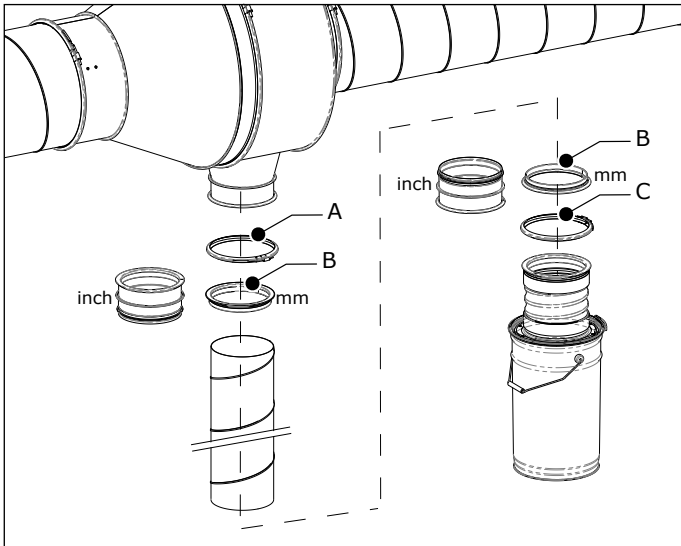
Staubbehälteranschluss über ein Vertikalrohr
